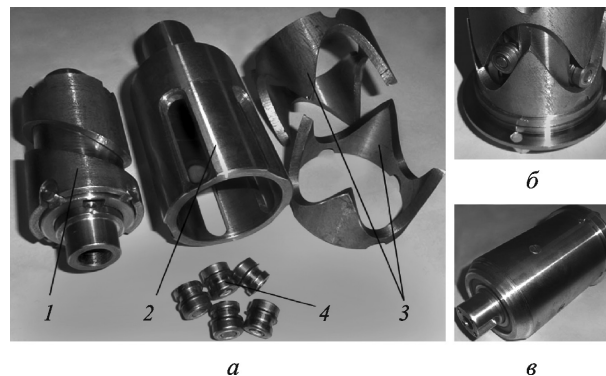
Основные детали ППТК (а), редуцирующий узел (б) и редуктор в сборе (в):
